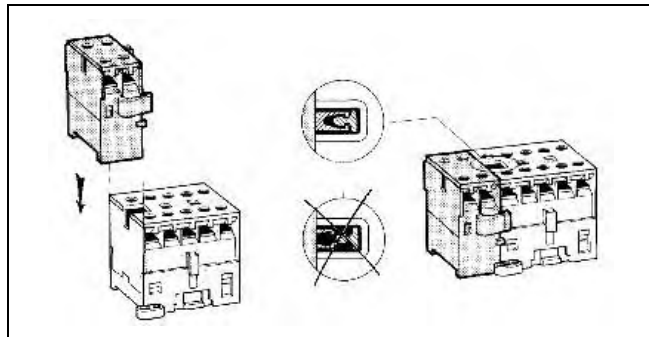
Minicontactor y contacto auxiliar montado lateralmente ensamblado
